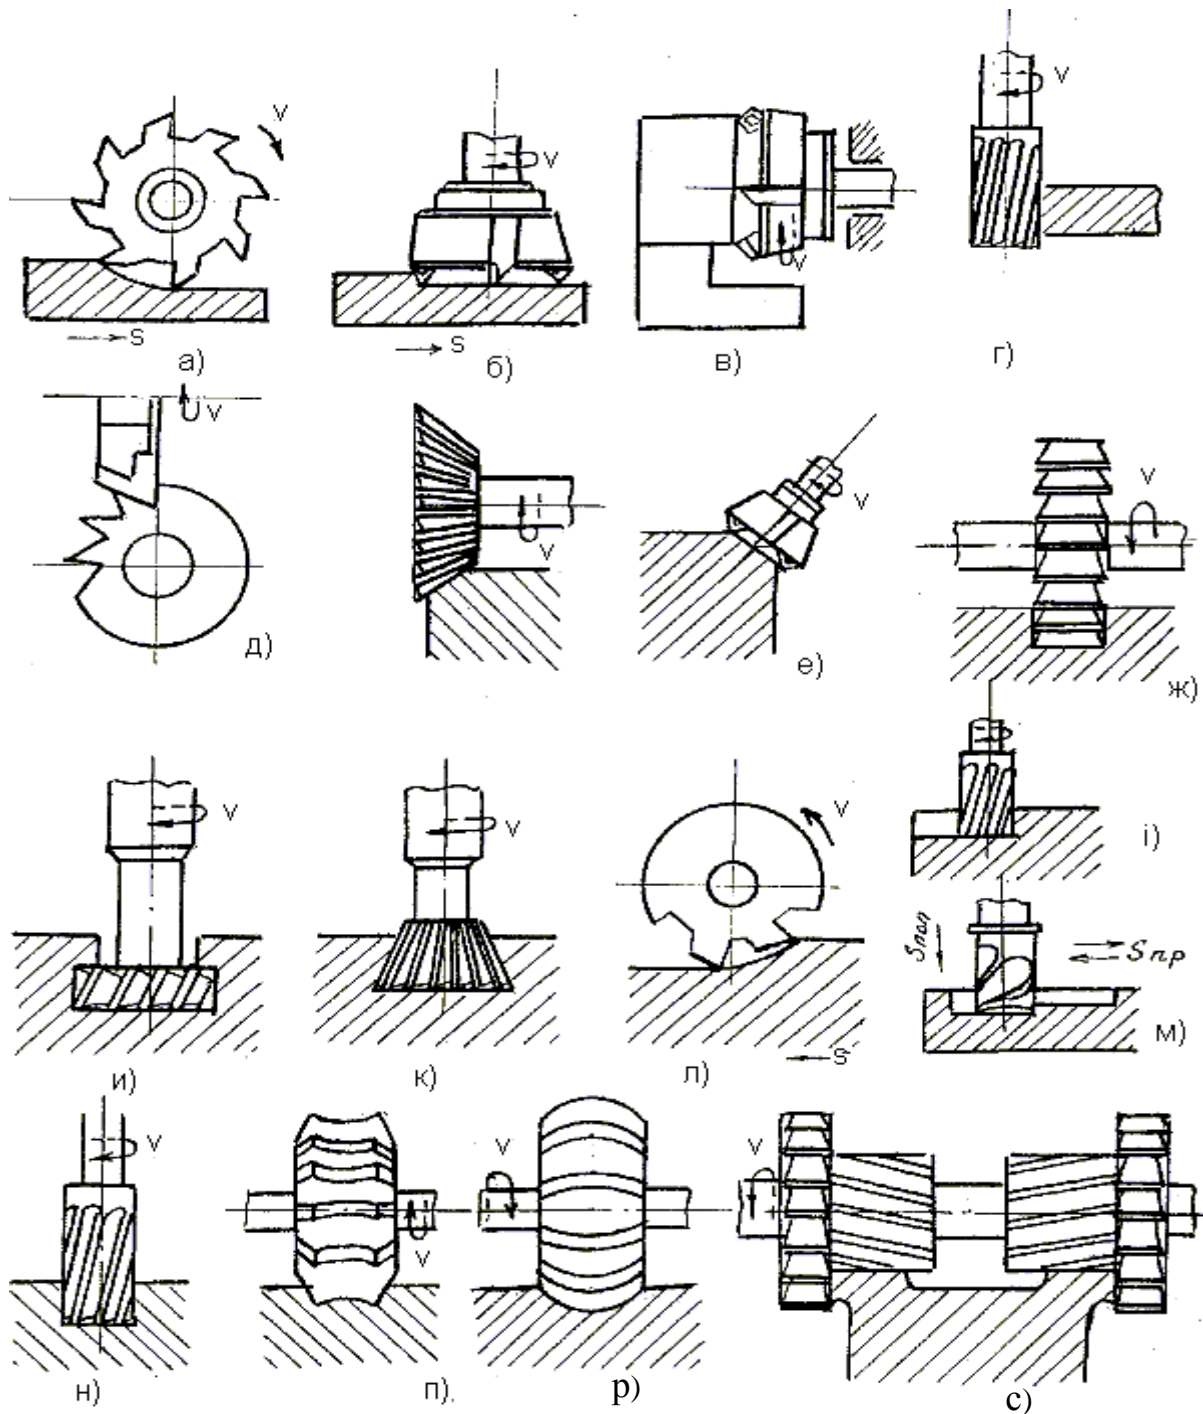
Приклади робіт, що виконуються на фрезерних верстатах
